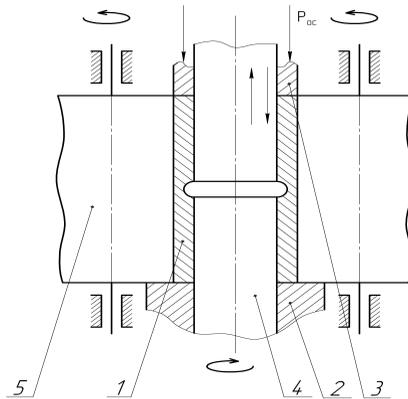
Схема многоциклового комплексного локального нагружения с приложением осевой силы для упрочнения изделия от внутренней поверхности: 1 – заготовка, 2 – упор, 3 – прижим, 4 – дорн, 5 – валковая матрица [1]
